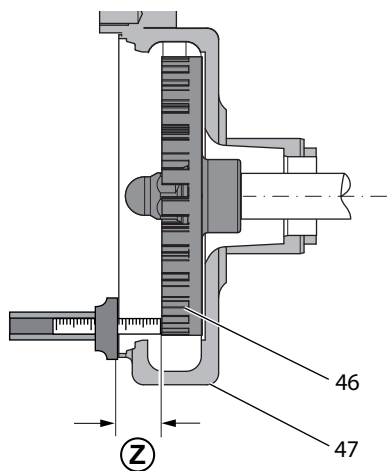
Измерение зазора "корпус насоса – рабочее колесо"
